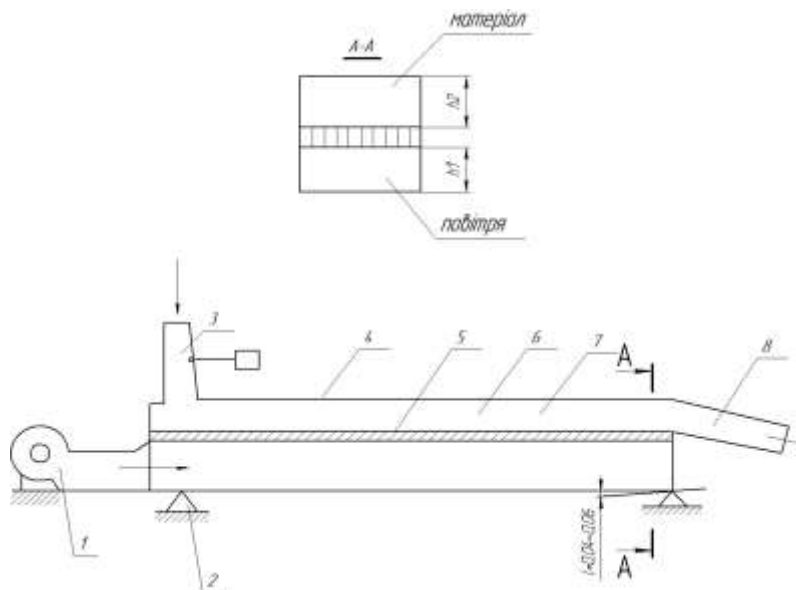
Схема аераційного транспортера: 1 – відцентровий вентилятор; 2 – опори; 3 – завантажувальний пристрій; 4 – металевий жолоб прямокутного перерізу; 5 – мікропориста перегородка; 6 – повітророзподільний канал; 7 – лоток для переміщення матеріалу; 8 – розвантажувальний пристрій
